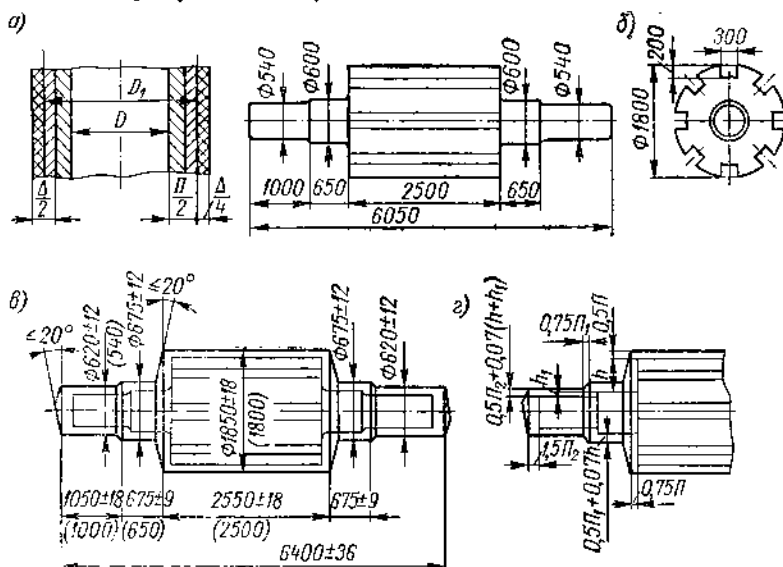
Пример составления чертежа поковки роторного вала с пазами дляковки на прессе: *а* — схема распределения припуска и допуска; *б* — чертеж поковки; *в* — чертеж роторного вала с пазами; *г* — расчет и распределение припусков
